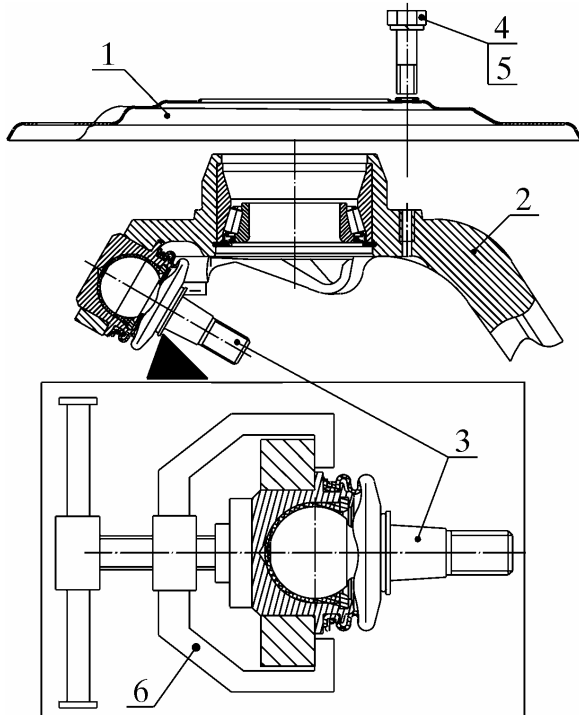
Снятие щита тормоза и выпрессовка нижнего шарнира из отверстия поворотной стойки:
